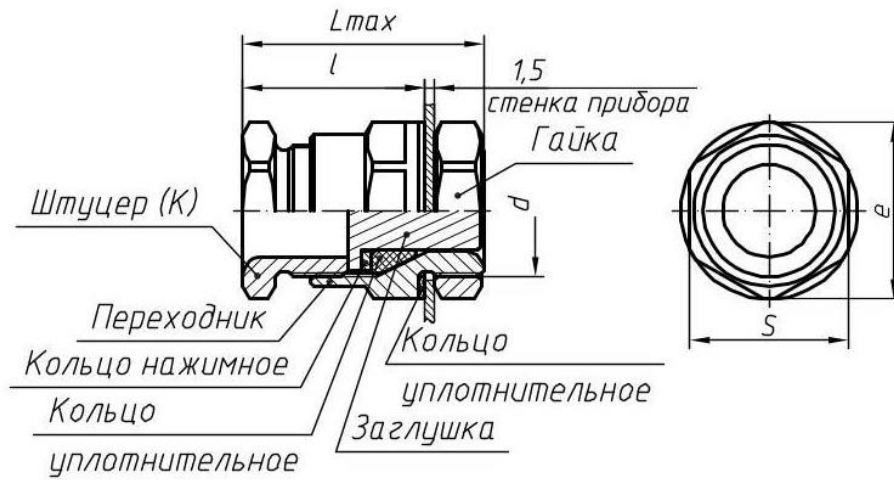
ЕхеКВУ-К – для открытой прокладки кабеля. Заглушка может быть изготовлена из полиамида 610 литьевого или металла, из которого изготовлен штуцер.
